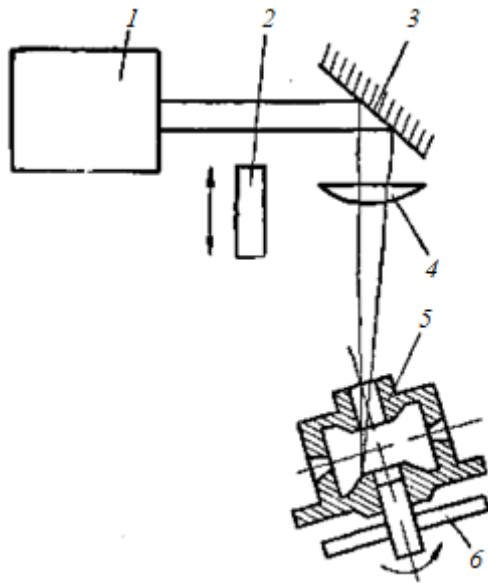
Схема лазерної установки для зміцнення циліндричних поверхонь:
